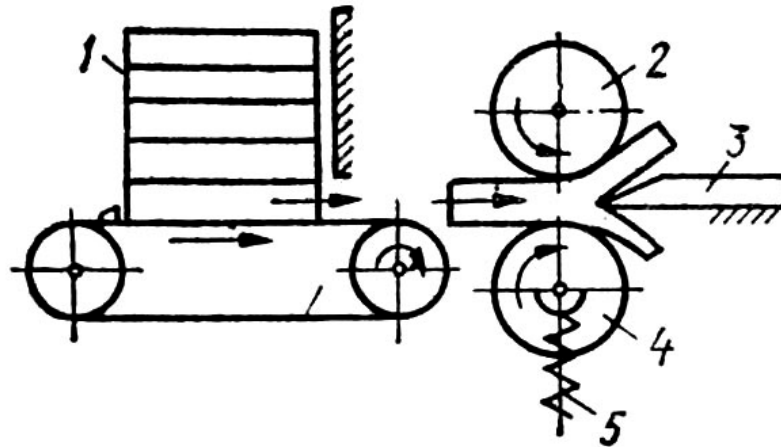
Функціональна схема двоїльної машини: 1 – магазинно-завантажувальний пристрій; 2 – верхній гладкий валик; 3 – нерухомий ніж; 4 – нижній рифлений валик; 5 – пружина [6]
